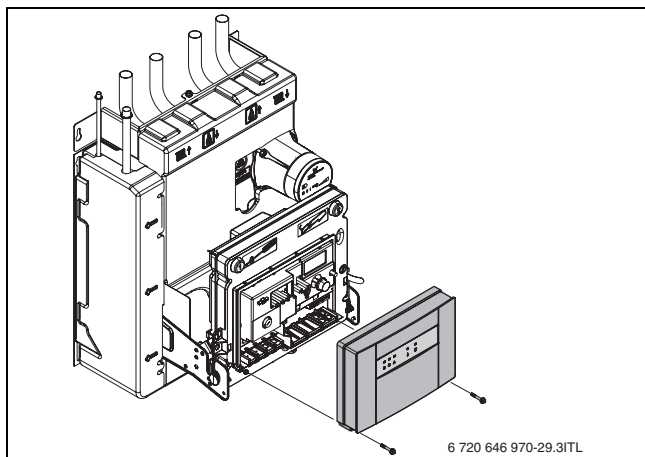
Frontabdeckung des Hybrid-Regelmoduls abnehmen
